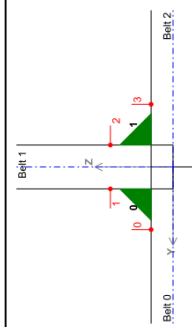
Schweißnahtdetail T_FD_EF
